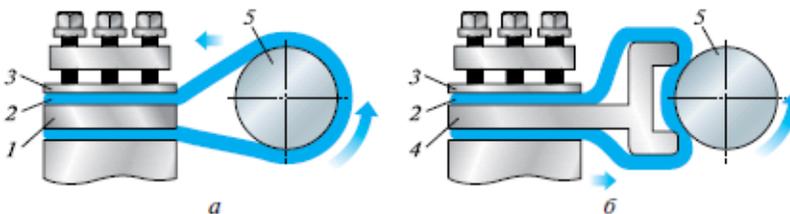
Полирование с помощью приспособлений: *а* — закрепление шлифовальной шкурки в резцедержателе; *б* — с применением «вилки» (1 — державка; 2 — шлифовальная шкурка; 3 — металлическая планка; 4 — «вилка»; 5 — изделие)
